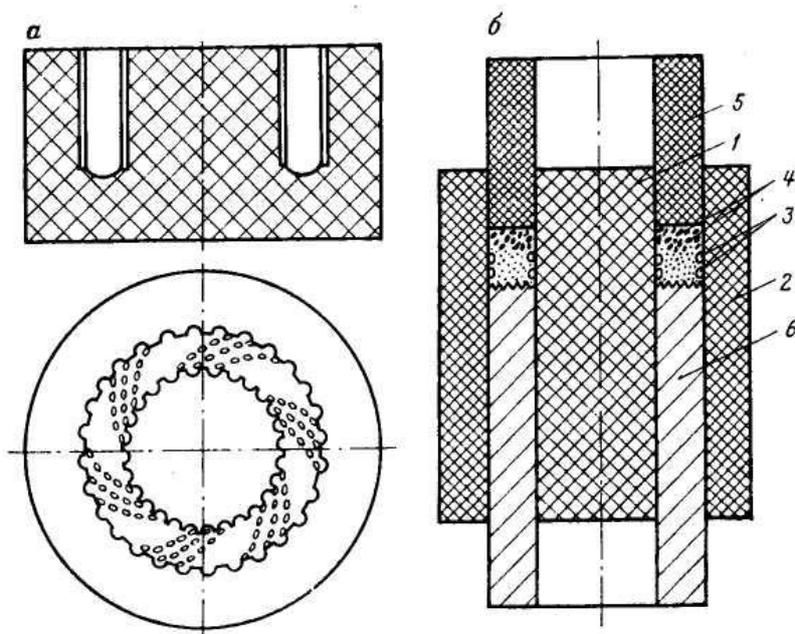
Схема пресс-форм для изготовления коронок методом:
